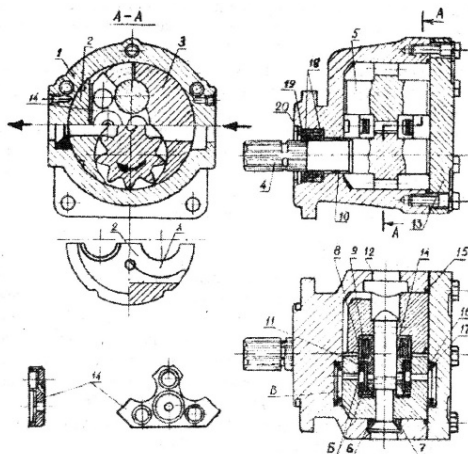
Односекционный шестеренный насос в круглом корпусе
